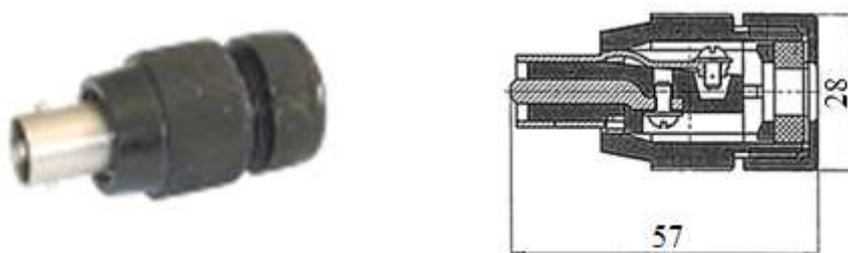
ШВ-51, внешний вид и габаритные размеры
